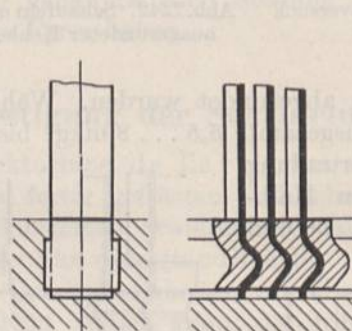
Befestigung der Brunner Maschinenfabrik.
